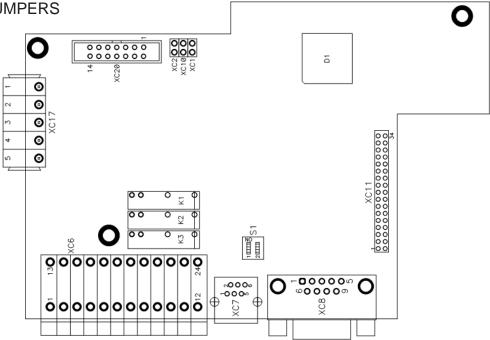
Cartão POS2 - Destaque Conectores e Jumpers
